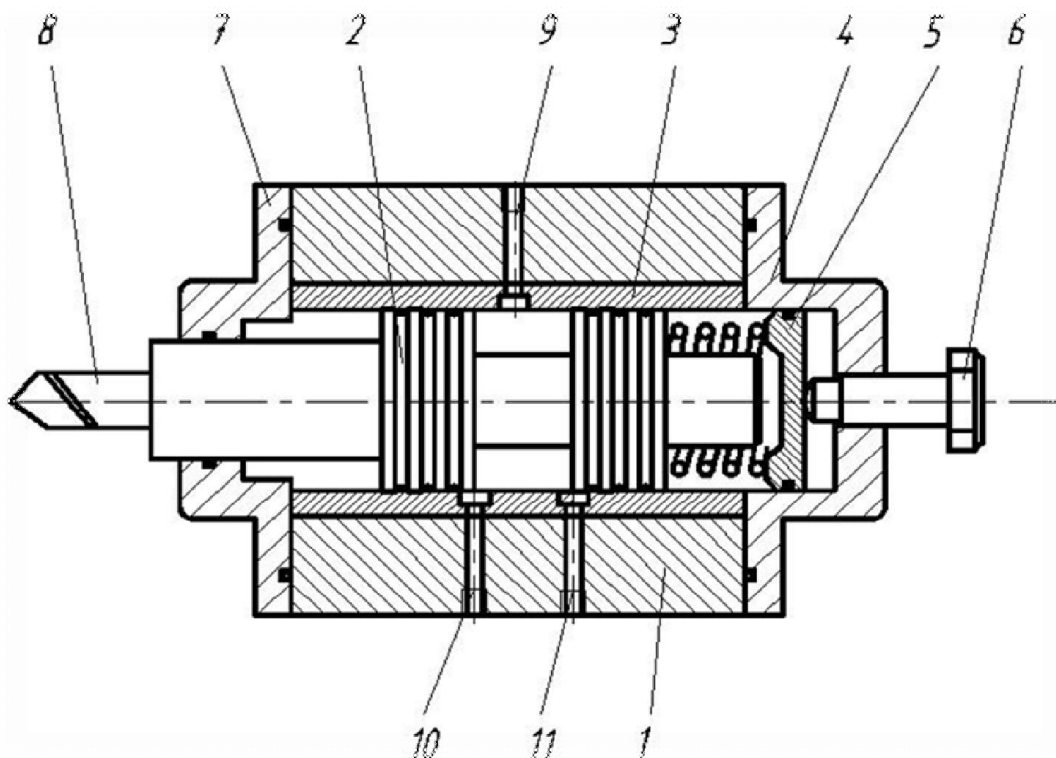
Конструктивная схема регулятора: 1- корпус; 2-плунжер; 3-гильза; 4, 7-крышка; 5-поршень; 6-винт регулировки поджатия пружины; 8-резец; 9, 10, 11-каналы.
